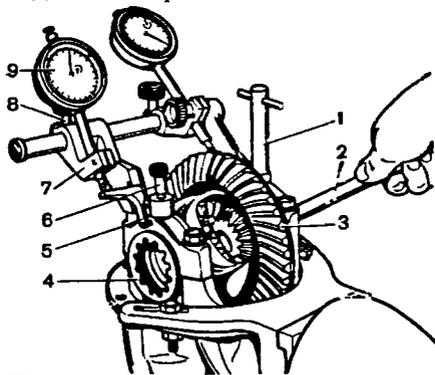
Проверка предварительного натяга подшипников коробки дифференциала приспособления А.95688/Р: 1 - винт крепления; 2 - ключ А.55085; 3 - ведомая шестерня; 4 - регулировочная гайка; 5 - промежуточный рычаг; 6 - винт крепления; 7 - кронштейн индикатора; 8 - винт затягивания кронштейна; 9 - индикатор для проверки предварительного натяга подшипников коробки дифференциала
